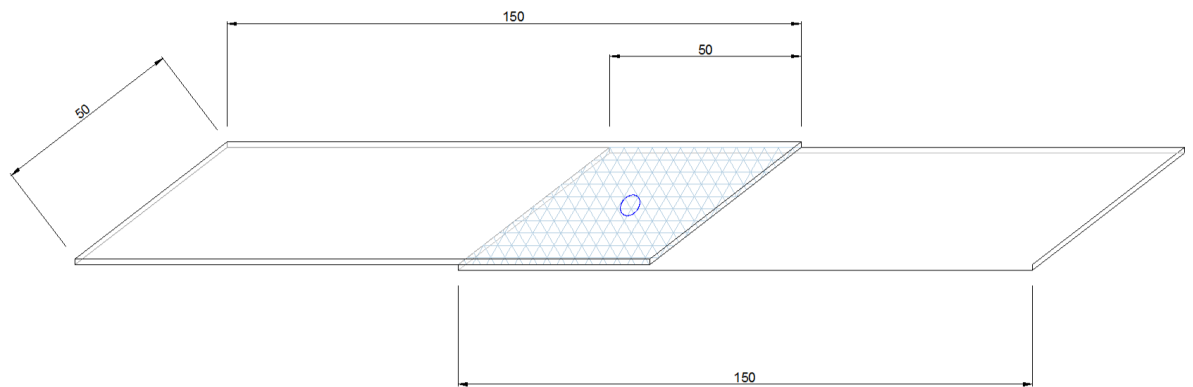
Dimensões do corpo de prova. Elaboração própria
